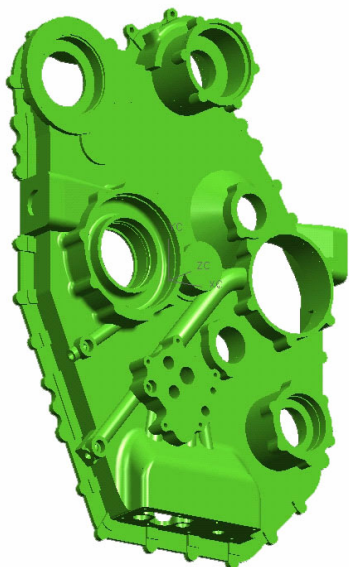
Корпус передний коробки приводов ВГТД МС-2
